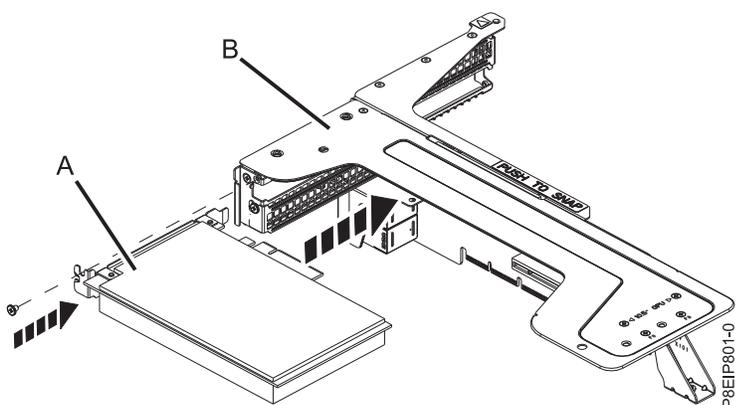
Inserindo um adaptador na posição 3 do riser PCIe
